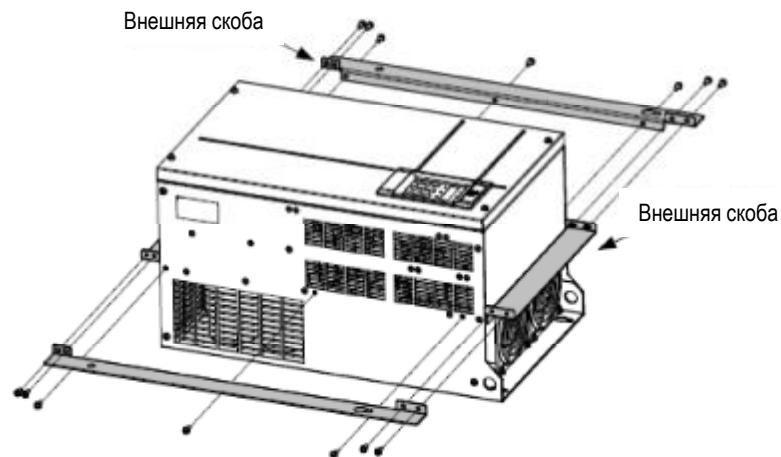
Встраиваемый монтаж для MD290 (металлический корпус)
